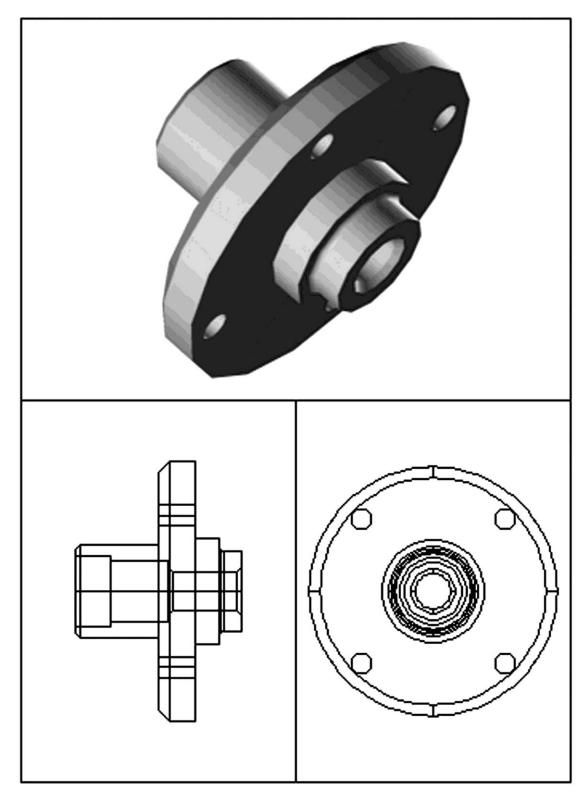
Образец выполнения 3D-модели детали по данным сборочного чертежа
